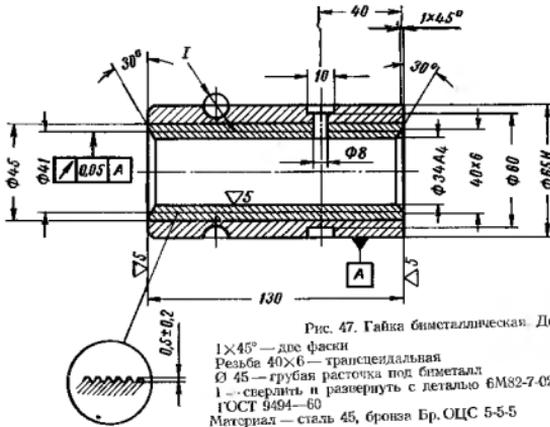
Гайка биметаллическая. Деталь 6М82-7-102
